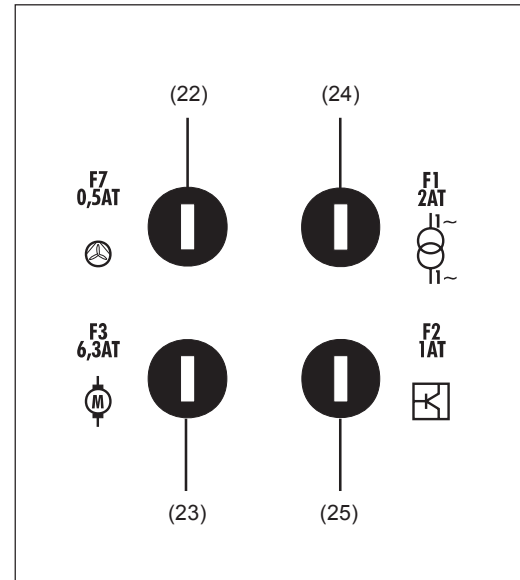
Sicherungen an der Innenseite des Schweißgerätes
